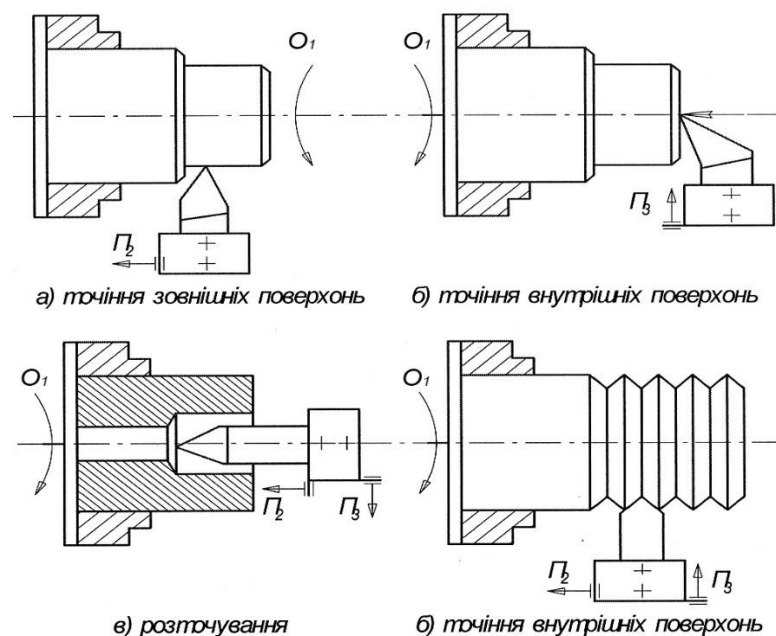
Типові схеми формоутворення поверхонь деталей на токарно-гвинторізних верстатах різцем
